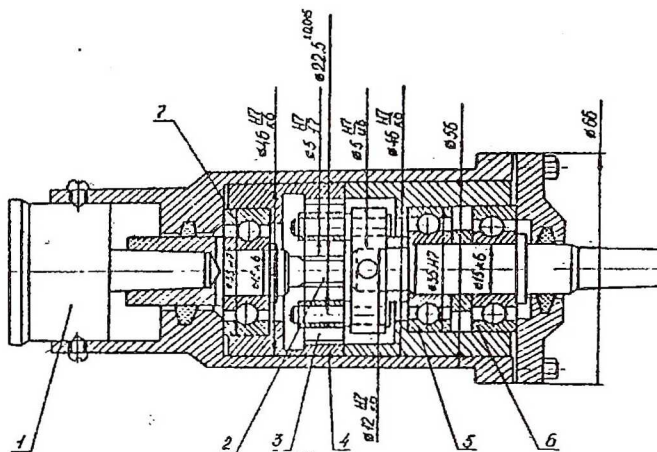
Малогабаритный планетарный редуктор для пневматической дрели.
